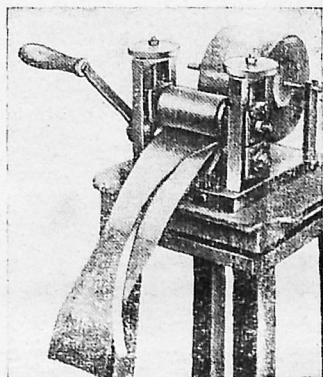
Приспособление для разрезания медной полосы на ленточки для уплотнителей.
